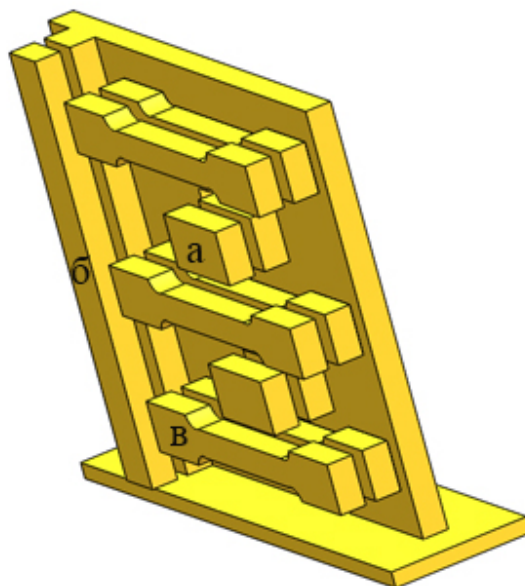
Схема вырезки образцов из аддитивной заготовки
